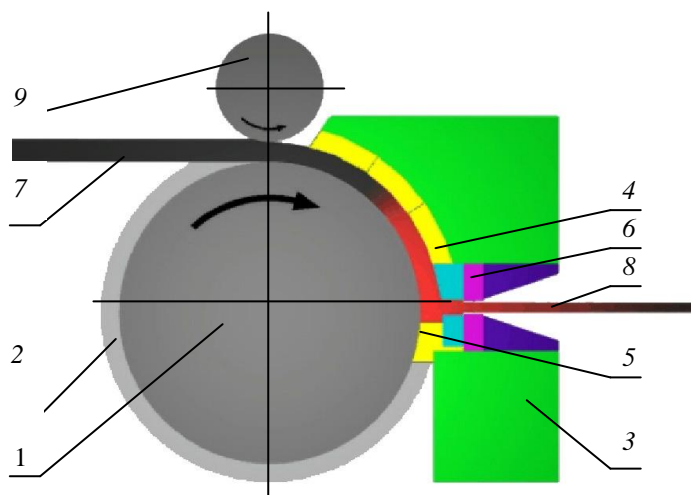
Принципиальная схема реализации процесса непрерывного прессования по способу Конформ [30]:
